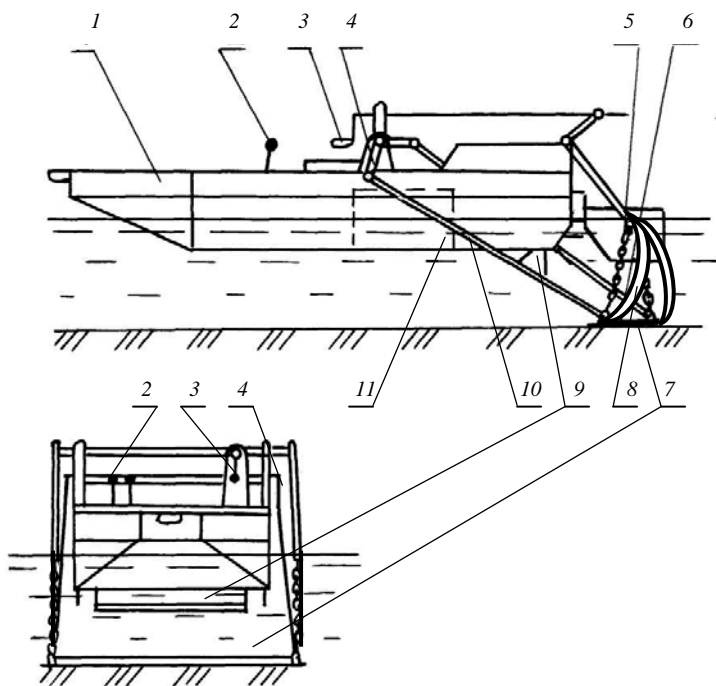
Схема косилки с волочащейся косой: 1 – мотобот; 2 – пост управления; 3 – рукоятка; 4 – кривошпы; 5 – рычаги; 6 – рули; 7 – волочащаяся горизонтальная коса; 8 – вертикальные косы; 9 – гребное колесо; 10 – тяги; 11 – силовая установка
